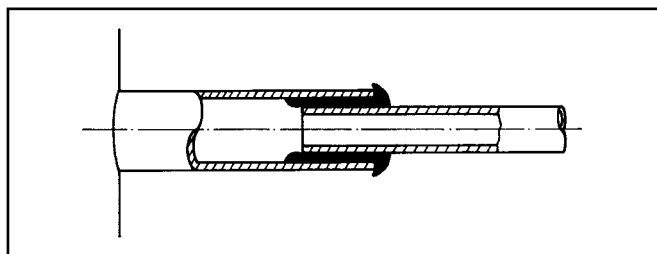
BRASAGEM COM EXCESSO DE MATERIAL DE ADIÇÃO
